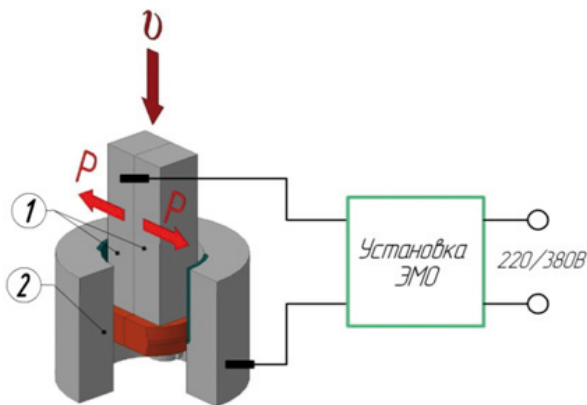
Схема процесса двусторонней ИЭМЗ: 1 – державка с инструментом; 2 – деталь
